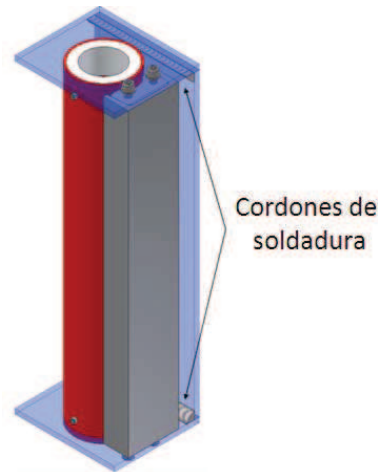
Diagrama de ubicación de la soldadura a corte.
